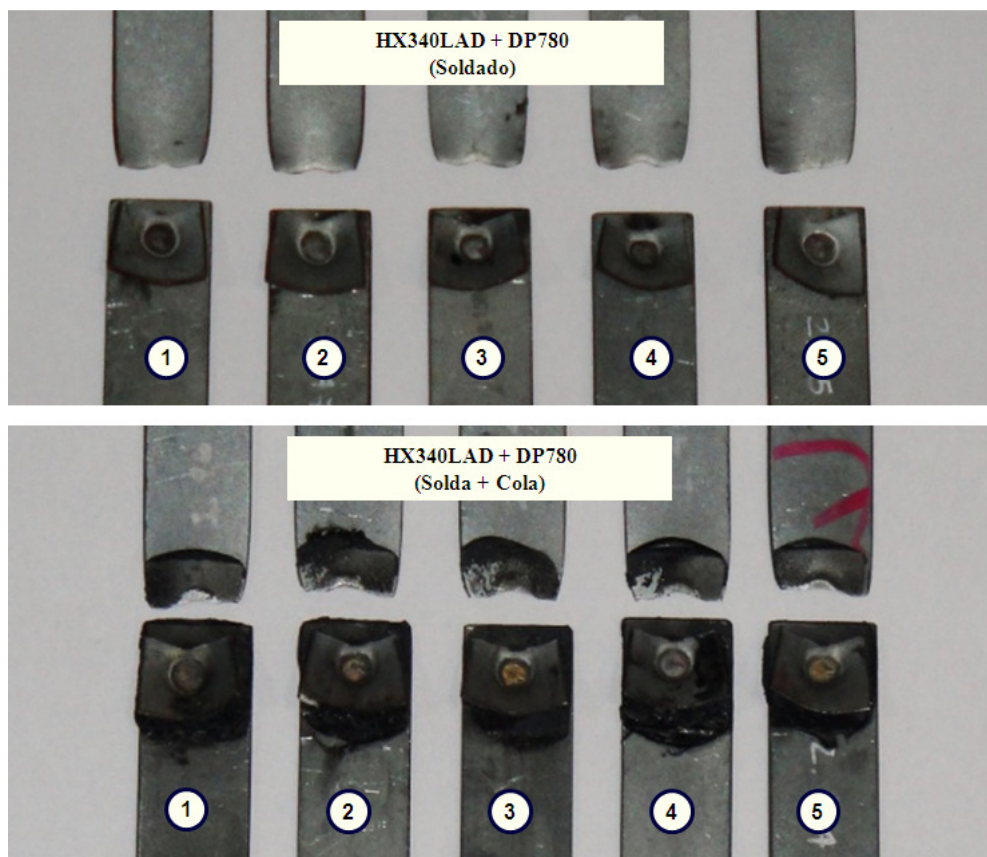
Detalhe das uniões soldadas rompidas HX340LAD + DP780.
